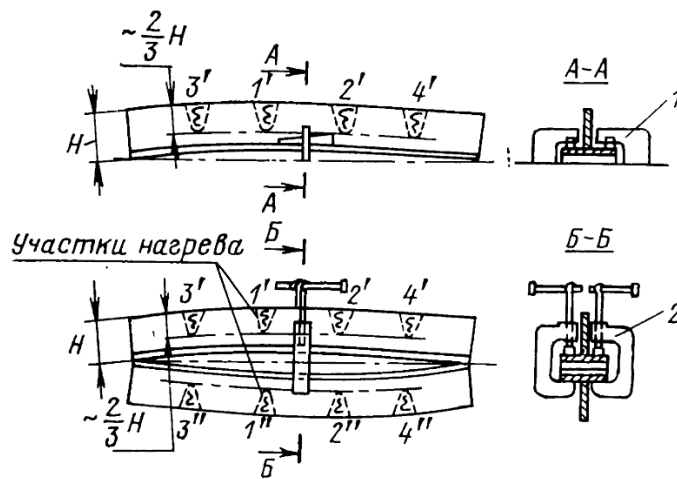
Схема правки сварных тавровых балок нагревом с принудительной посадкой.
